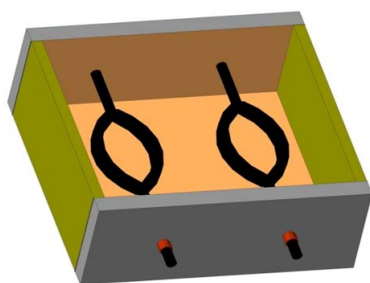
Схематичное изображение формы закладных элементов станины настольного станка для ультразвуковой сварки полимеров
